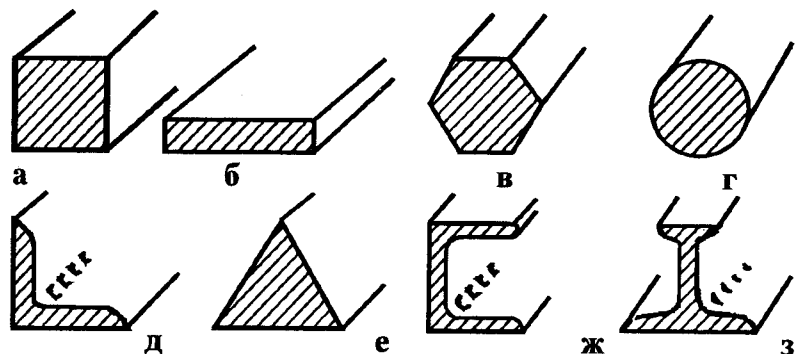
Сортовой прокат: а — квадрат; б — полоса; в — шестигранник; г — круг; д — уголок; е — треугольник; ж — швеллер; з — рельс
